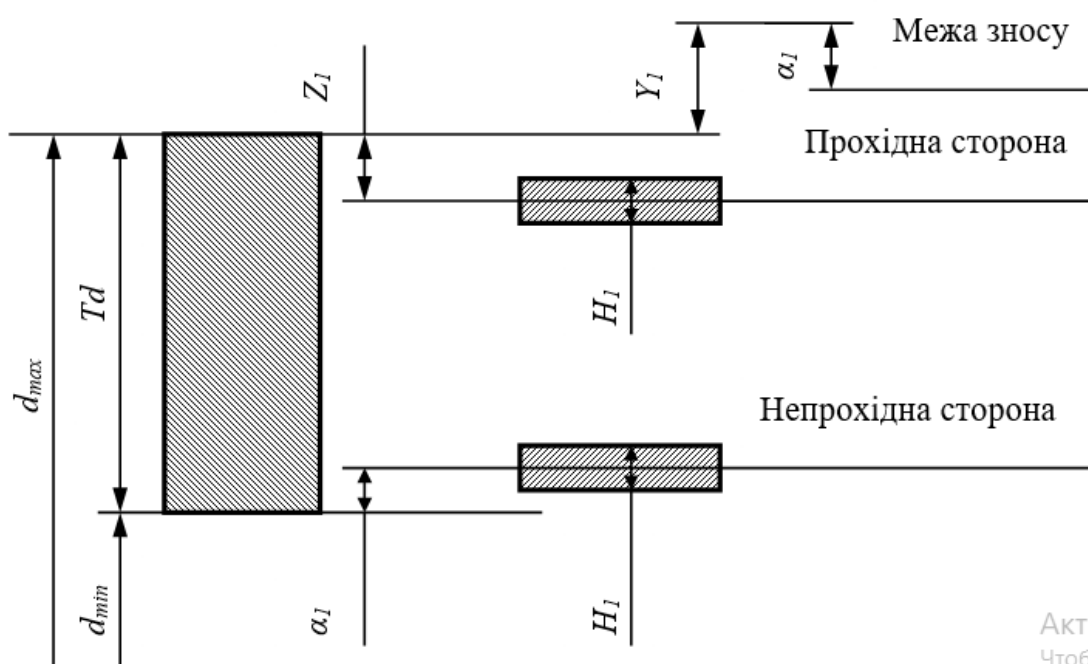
Схема розташування поля допусків гладенького предельного калібру – скоби для контролю валу
